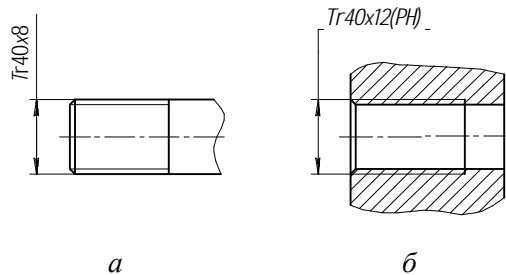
Нанесение размеров трапецеидальной резьбы:
